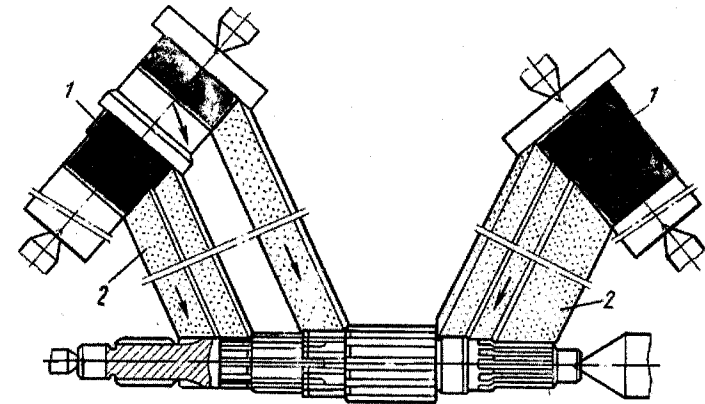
Совмещенное шлифование цилиндрических и торцовых поверхностей вала и правка кругов блоками алмазных роликов:
